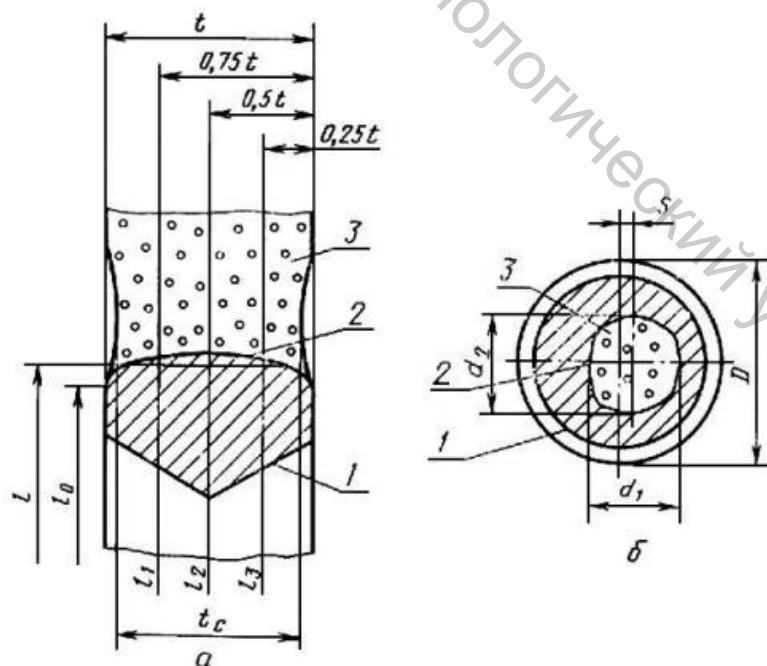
Схемы изломов: а – плоских образцов типов 1, 3 и 4, б – цилиндрического образца типа 2: 1 – граница надреза; 2 – контур усталостной трещины; 3 – статический долом
